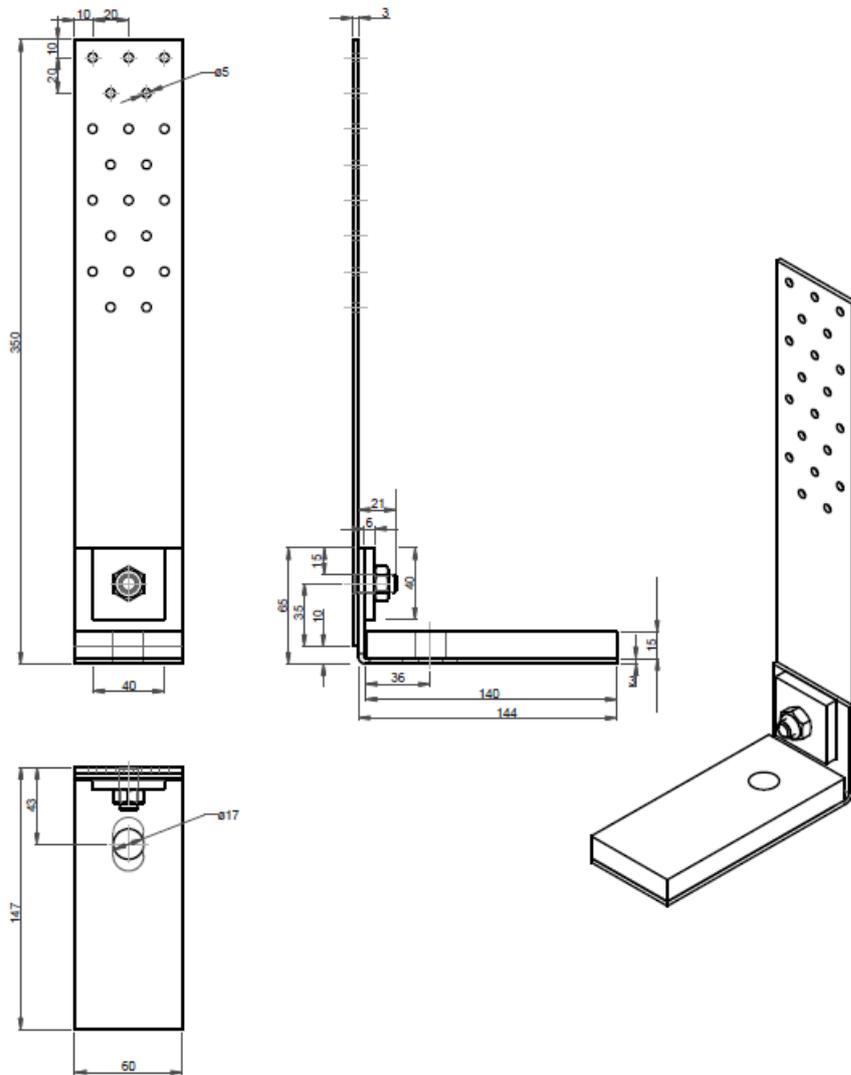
HT2-G-Druckplatte-lang-Z-316
